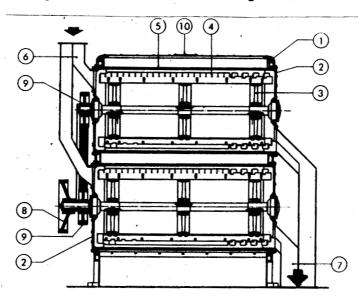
DESGERMINADOR HORIZONTAL DE IMPACTO,
